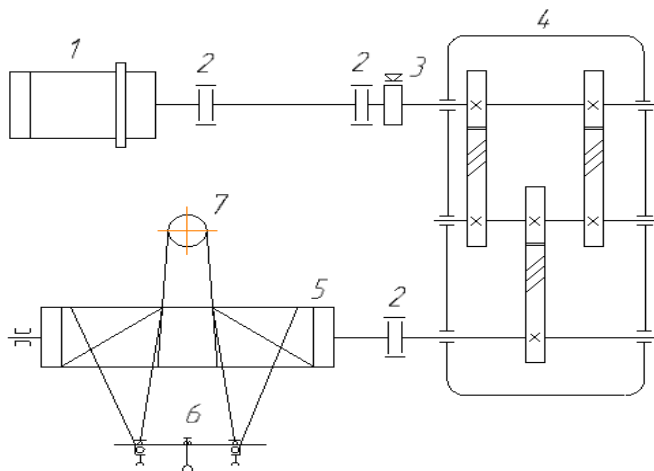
Кінематична схема механізму підйому головного гака: 1 - двигун; 2 - муфта; 3 - гальмо; 4 - редуктор; 5 - барабан; 6 - поліспаст; 7 - нерухомий блок поліспасти.
